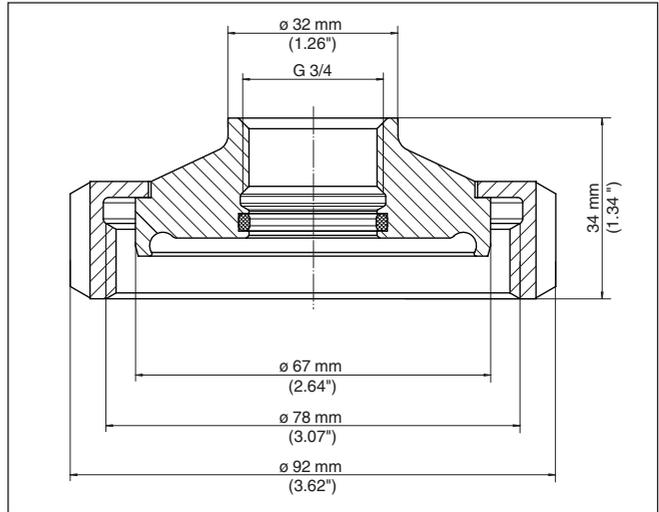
Dimensiones adaptador de rosca G^{3/4} (DIN 3852-X) a racor rosca-
